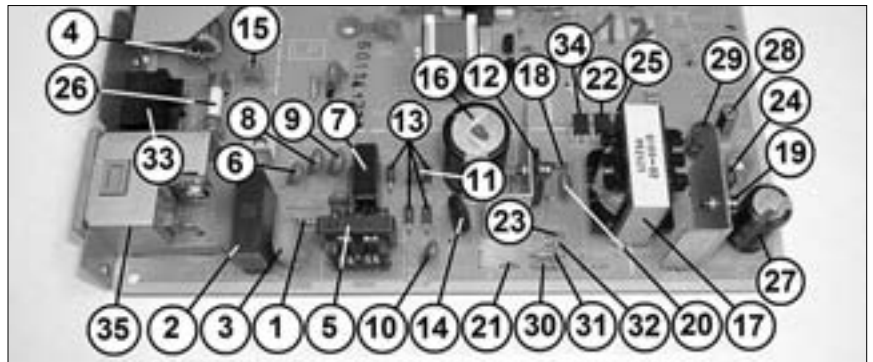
Часть 1 платы Power supply PCB, вид сверху
